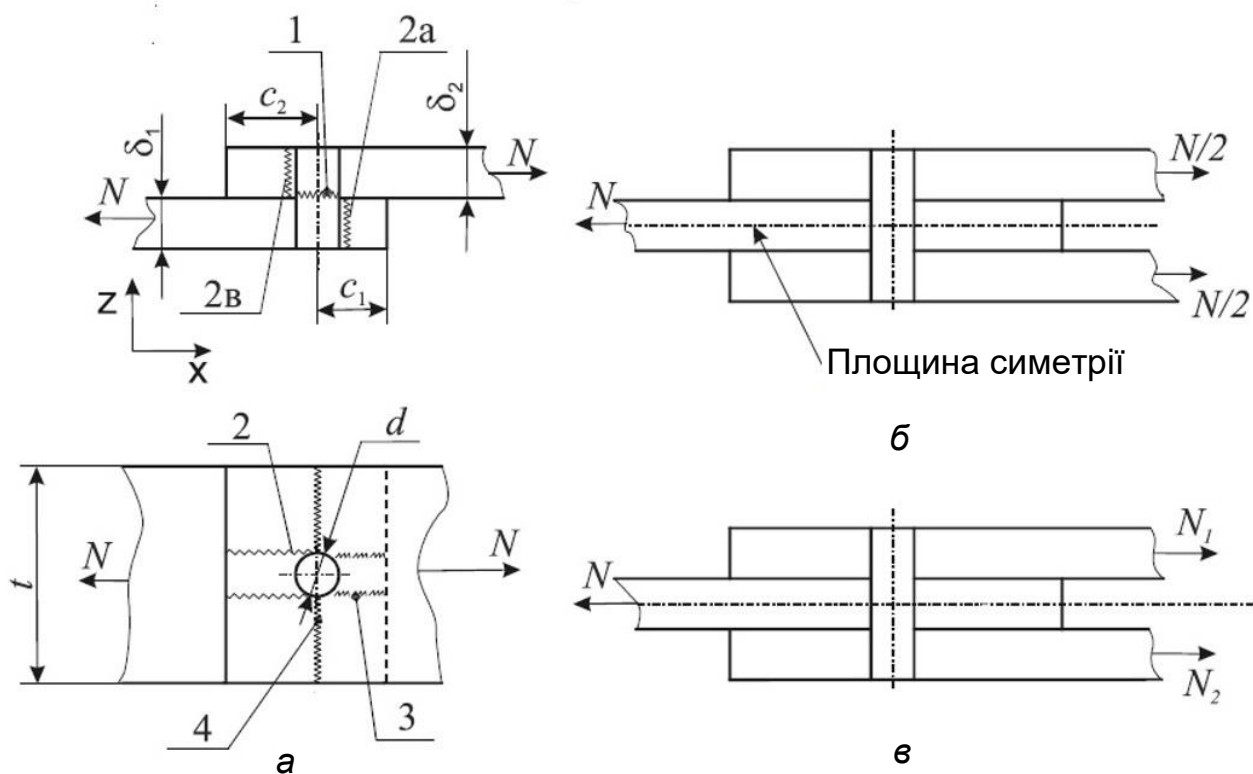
Типовий елемент механічного з'єднання метал – композит
